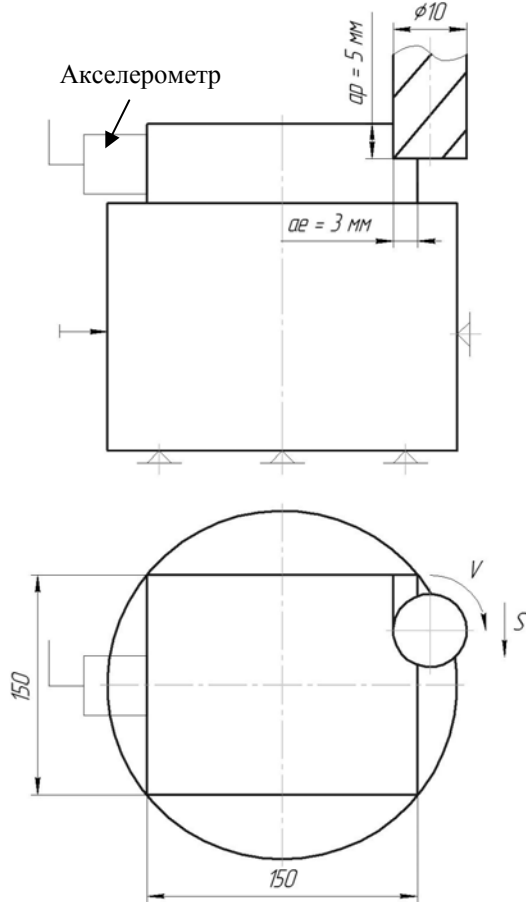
Схема установки обрабатываемой детали, фрезы и акселерометра во время эксперимента.
